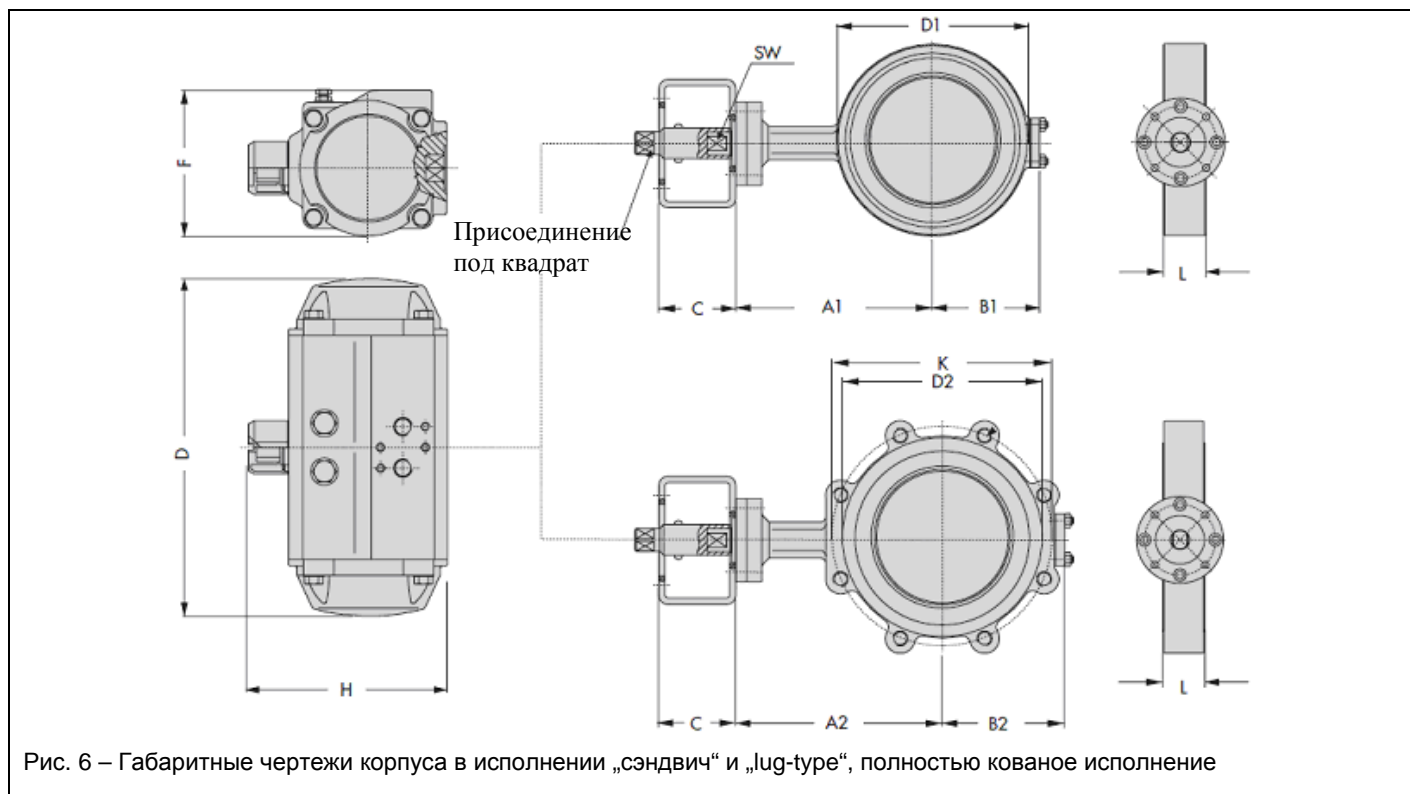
Габаритные чертежи корпуса в исполнении „сэндвич“ и „lug-type“, полностью кованое исполнение
